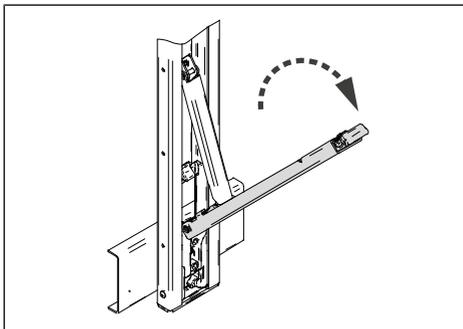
Virar a alavanca de bloqueio para baixo
